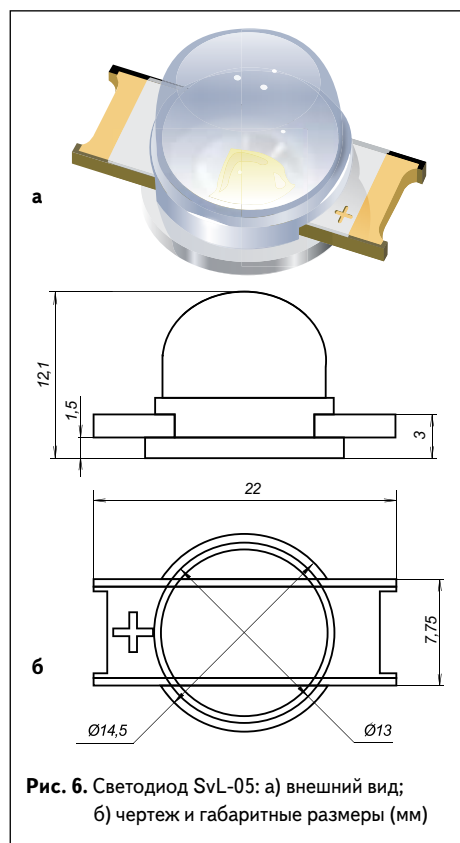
Светодиод SvL-05: а) внешний вид; б) чертеж и габаритные размеры (мм)
